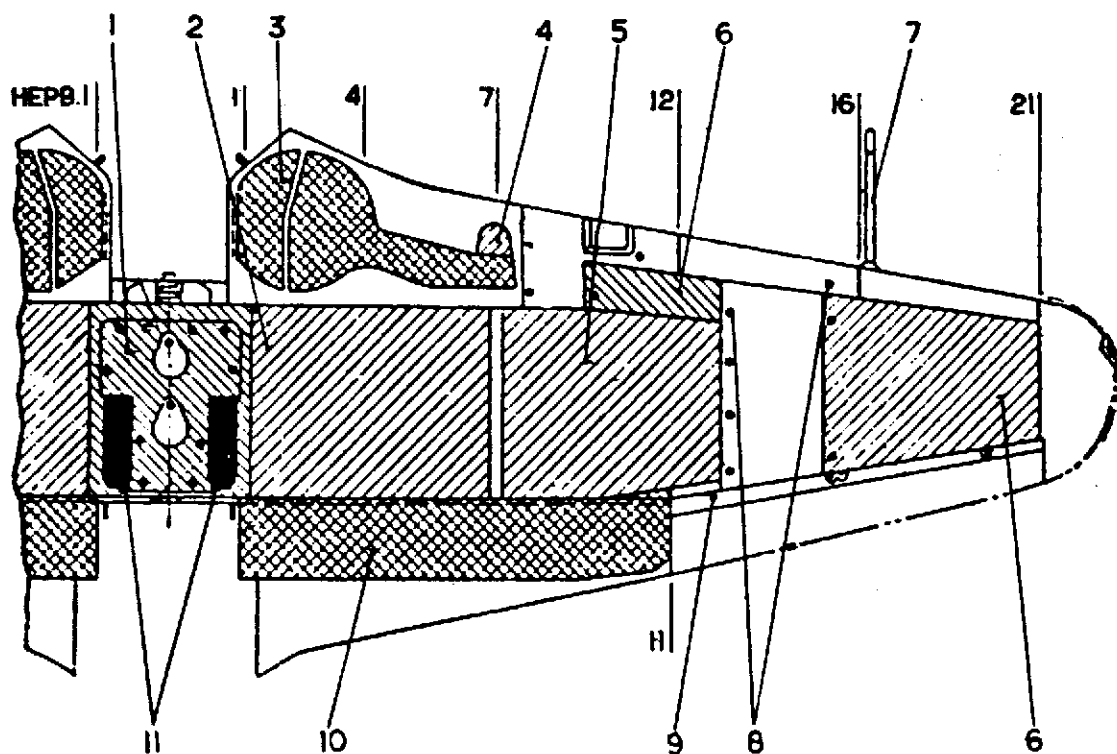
СХЕМА КРЫЛА (ВИД СНИЗУ)
